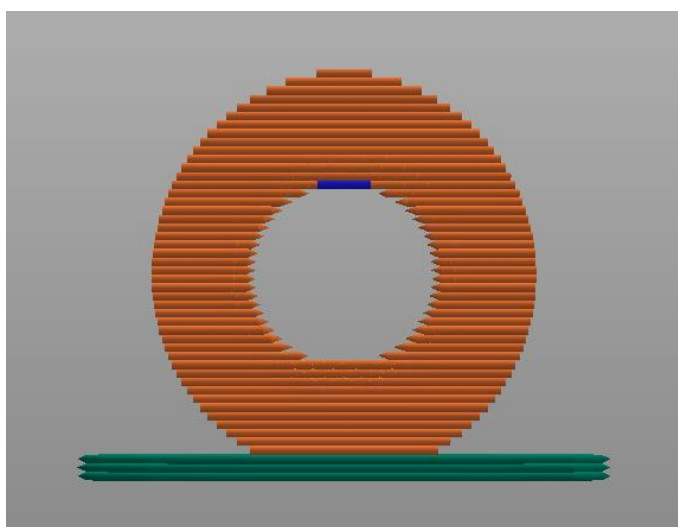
Konstrukční řešení kladky pro Adaptér 2
